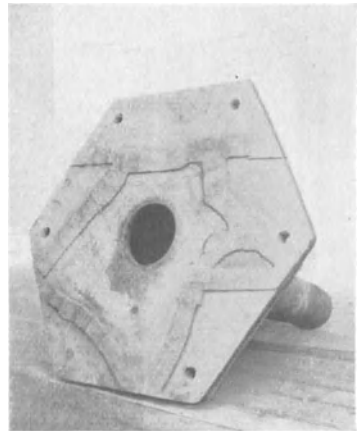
Ständerplatte nach der Schweißung.
